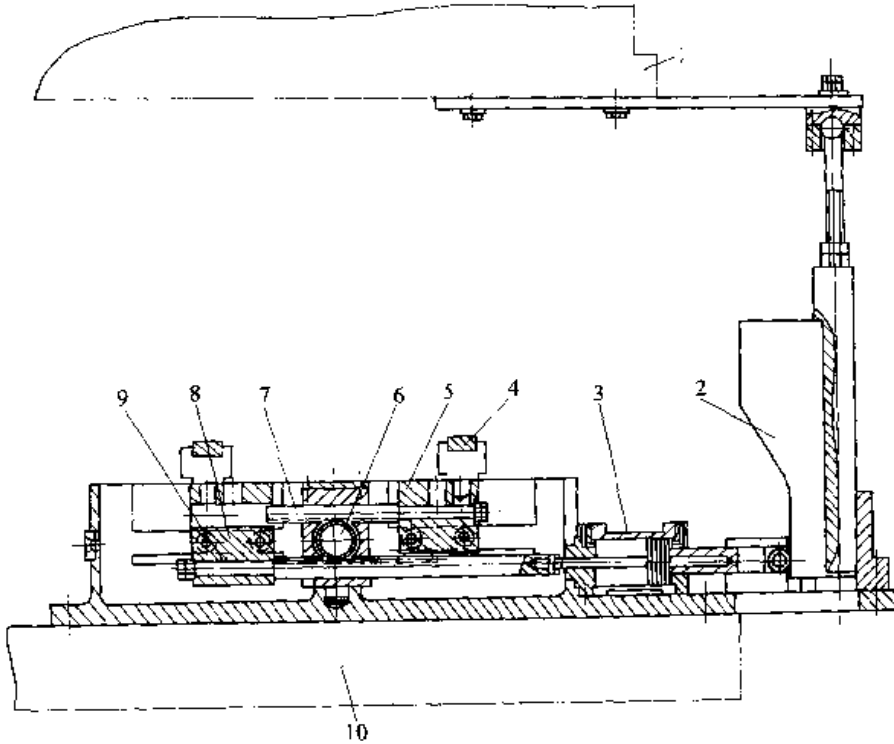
斜楔齿轮齿条传动式横向夹紧驱动机构
